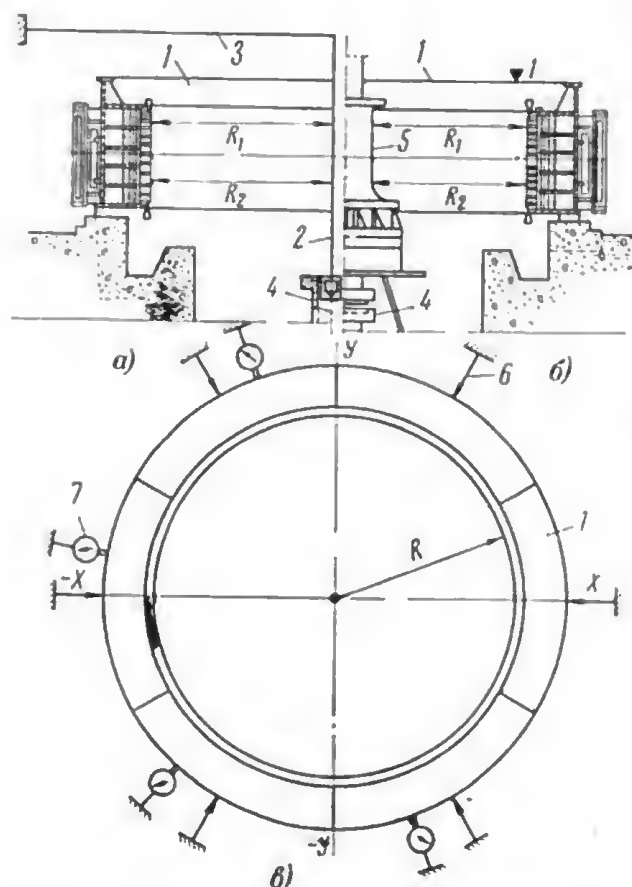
Схема выверки статора генератора. а — выверка по осевой струне; б — выверка по валу генератора; в — схема перемещений статора и устранения эллиптичности; 1 — статор; 2 — осевая струна с отвесом; 3 — горизонтальные струны; 4 — вал турбины; 5 — вал генератора; 6 — домкраты; 7 — индикаторы.
